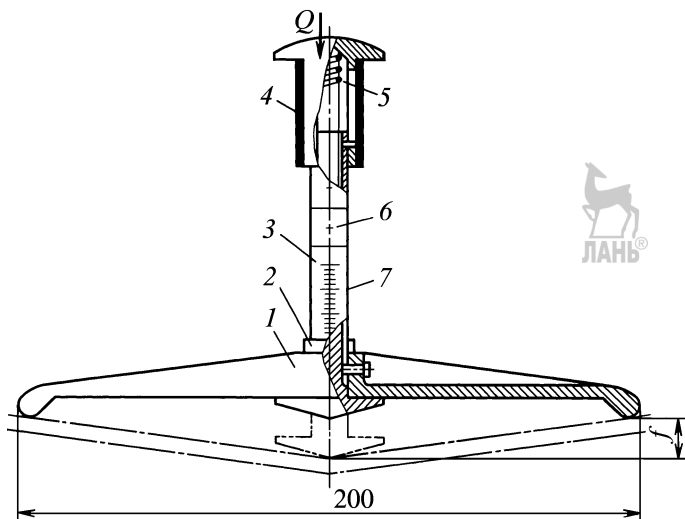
Приспособление для контроля натяжения приводных ремней
